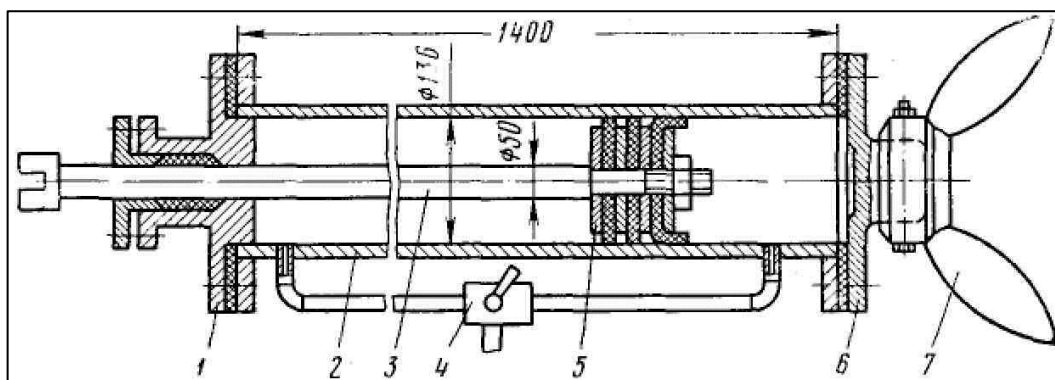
Конструкция гидравлического толкателя для передвижки забойных водоводов: 1 - верхняя крышка с сальником; 2 - цилиндр; 3 - шток; 4 - четырехходовой кран для подачи воды; 5 - поршень; 6 - нижняя крышка; 7 - упор
